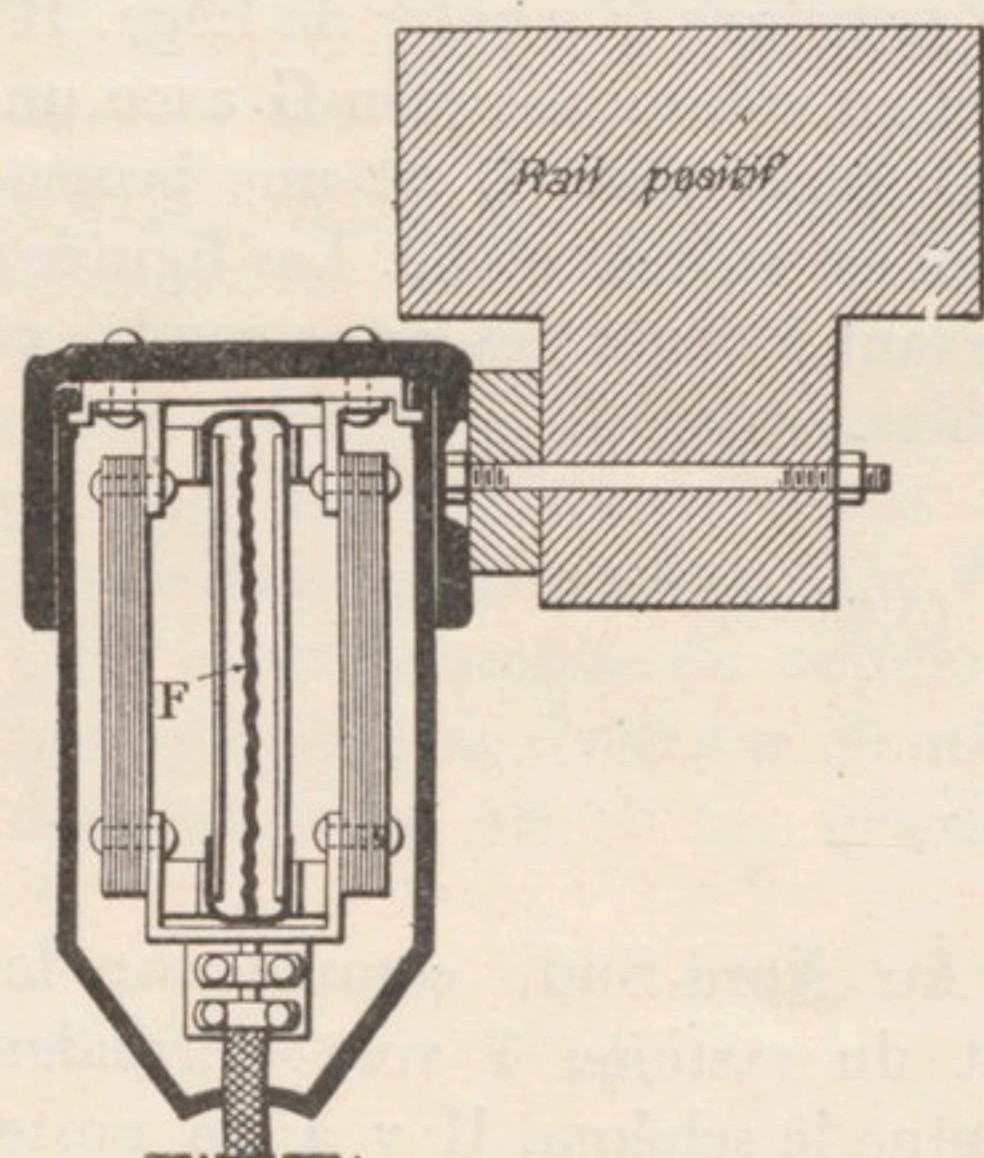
Coupe de la prise de courant sur le rail isolé.
